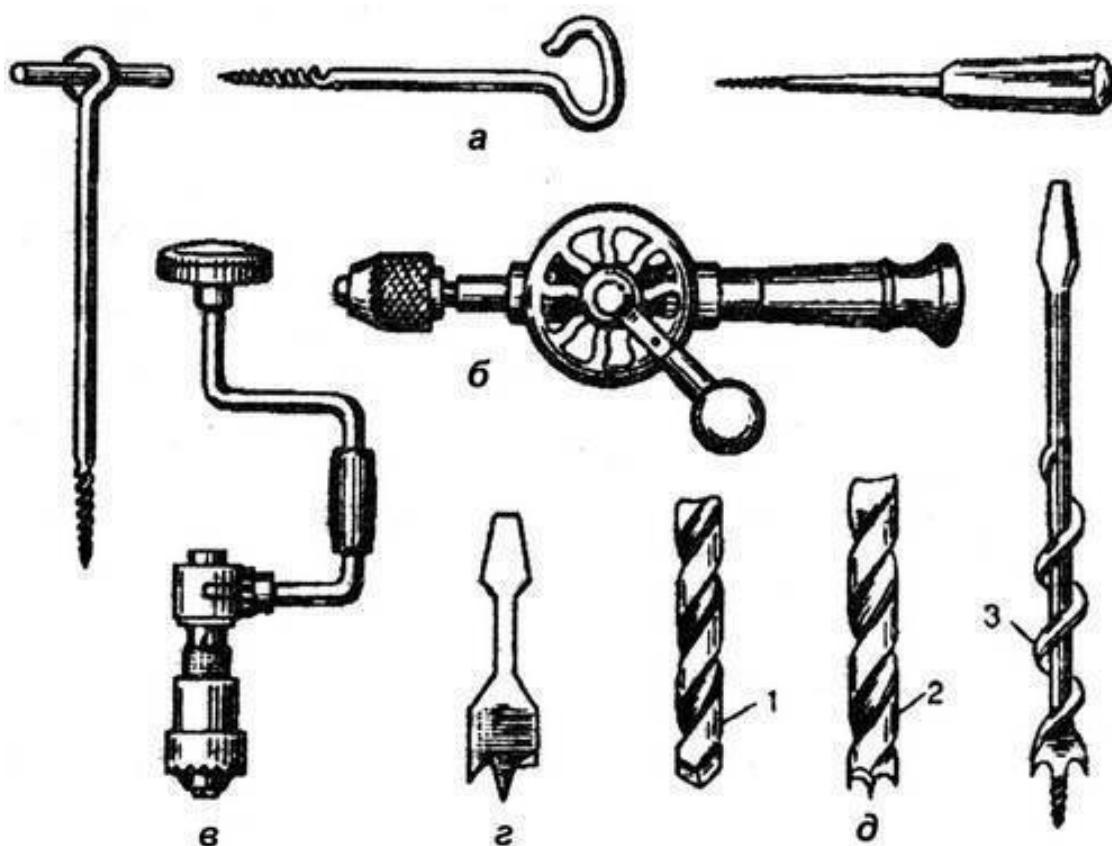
Устройства для сверления: *а* – буравы; *б* – ручная дрель; *в* – коловорот; *г* – перка; *д* – сверла (1 – по металлу; 2 – по дереву; 3 – винтовые)
